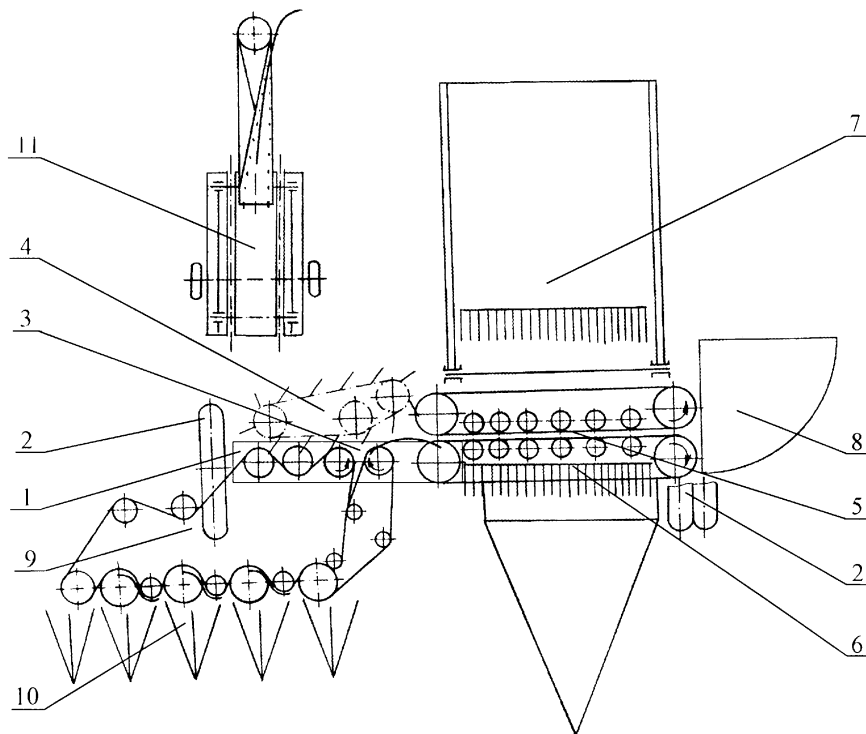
Схема льнозбиральної машини з розробленими змінними бральним і підбирально-повертальним апаратами: 1 – рама; 2 – колісний хід; 3 – механізм приводу; 4 – поперечний транспортер; 5 – затискний транспортер; 6 – очісуючий апарат; 7 – транспортер вороху; 8 – розстилочний щит; 9 – бральний апарат; 10 – подільники; 11 – підбирально-повертальний апарат
